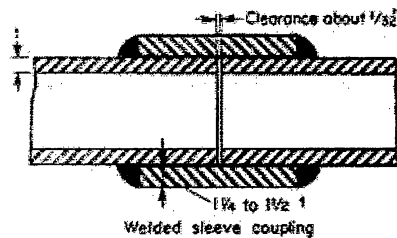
Ejemplo de uniones típicas por soldadura de filete.
